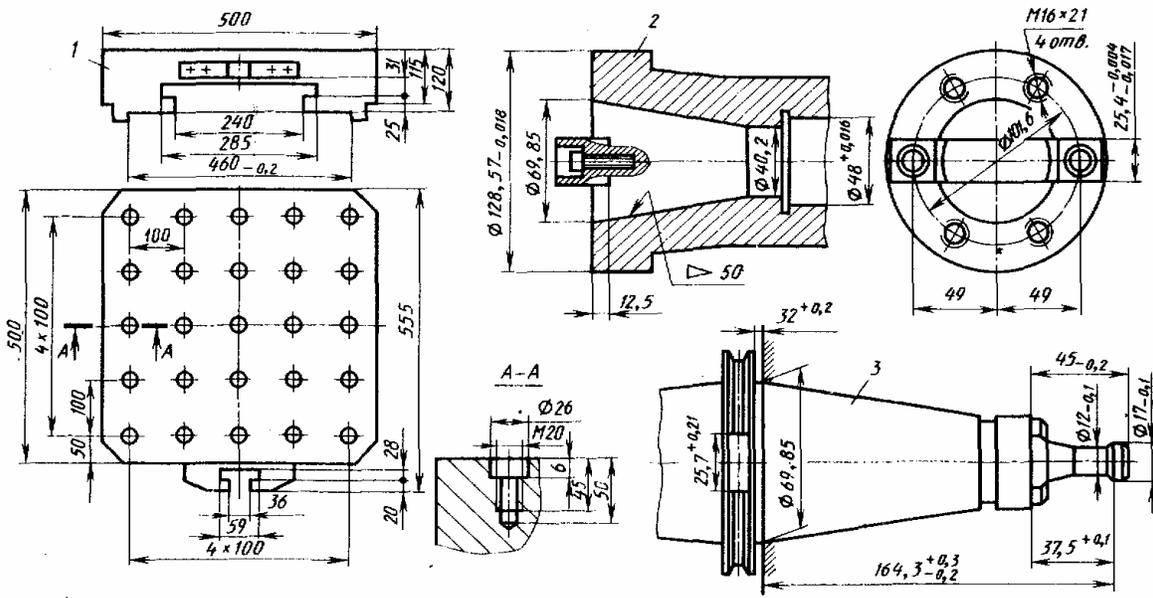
Установочные базы сверлильно-фрезерно-расточного станка мод. ИР500МФ4 (1 – плита спутника; 2 – шпиндель; 3 – инструментальная оправка)
